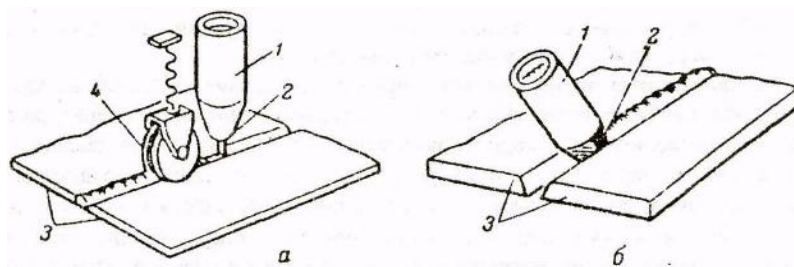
Схемы бесконтактной (а) и контактно-экструзионной (б) сварки расплавом: 1-экструдер, 2- мундштук экструдера; 3- свариваемые детали; 4— прикатывающий ролик
